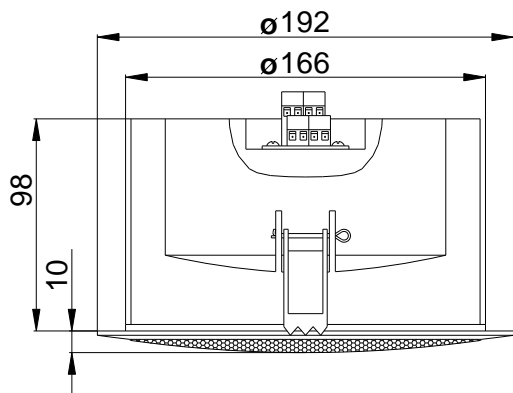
Внешний вид и габаритные размеры корпуса оповещателя
